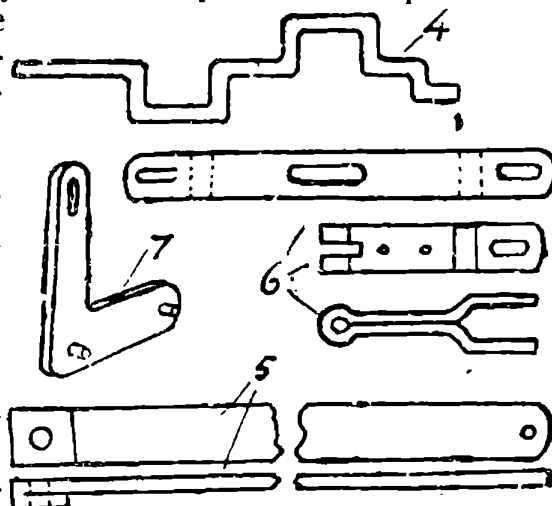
Коленчатый вал, 5, 6, 7 — рычаги золотниковой передачи
